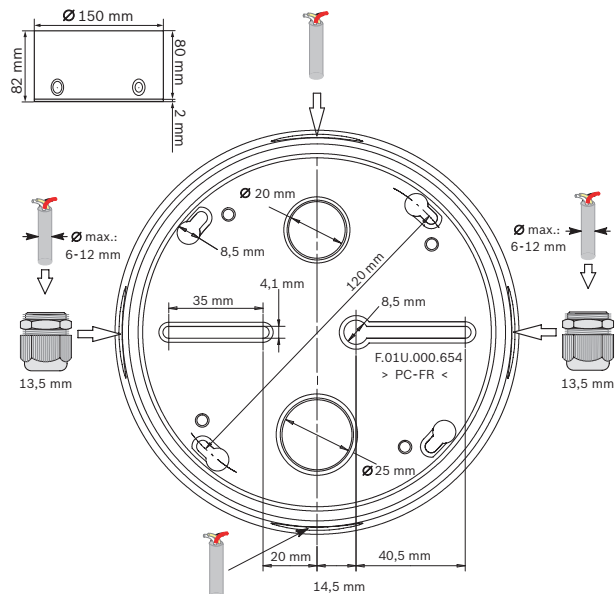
Коробка для установки на поверхность FAA-500-SB-H
